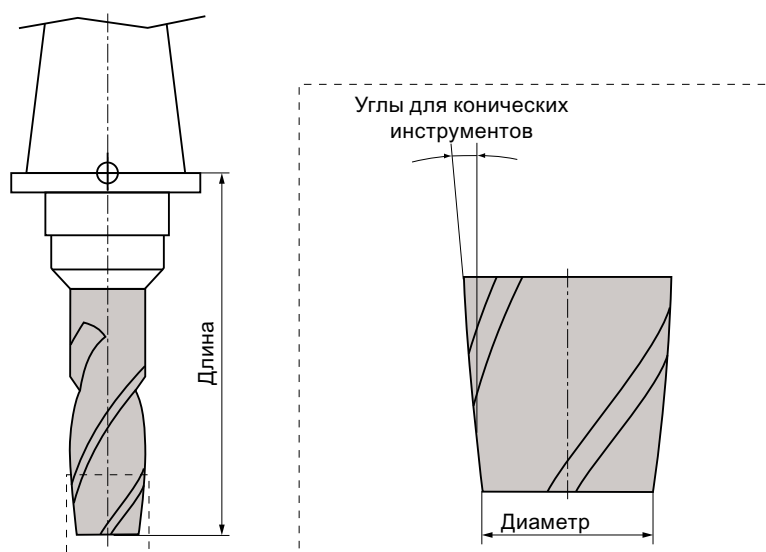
Тип инструмента 3D на примере конической фрезы (тип 155)
